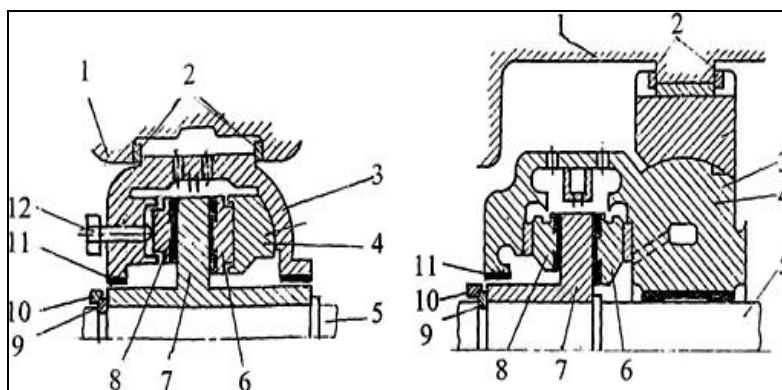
Подшипники скольжения: а – упорный; б – упорно-опорный; 1 – крышка корпуса подшипника; 2 – переднее и заднее установочные кольца (каждое из 3 сегментов); 3 – разъемная сферическая обойма; 4 – разъемный сферический вкладыш; 5 – вал; 6 – рабочая упорная колодка; 7 – упорный диск (гребень); 8 – установочная (нерабочая) упорная колодка; 9 – кольцо из 2 половин; 10 – кольцо; 11 – маслоудерживающий баббитовый пояс; 12 – установочный болт
